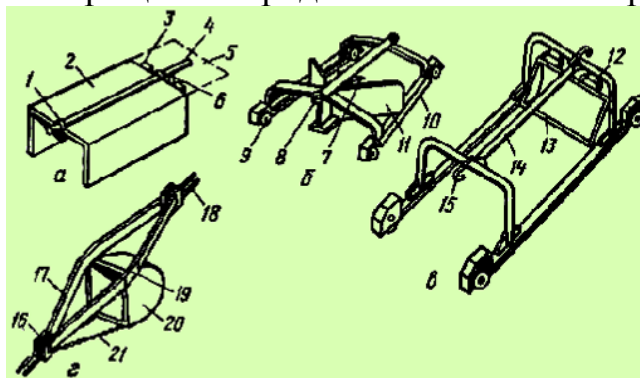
Типы скреперов: а – короб; б – стрела; в – каретка; г – лопата; 1 – направляющая; 2 – короб; 3 – шарнир; 4 – тяговый орган; 5 – стенка; 6 – тяга; 7 – упор; 8 – тяговый крюк; 9 – опорный ролик; 10 – рама; 11 – поворотная лопасть; 12 – шарнир; 13 – скребок; 14 – рама; 15 – тяговый крюк; 16 – зажим; 17 – тяга; 18 – трос; 19 – шарнир; 20 – скребок; 21 – цепь.
